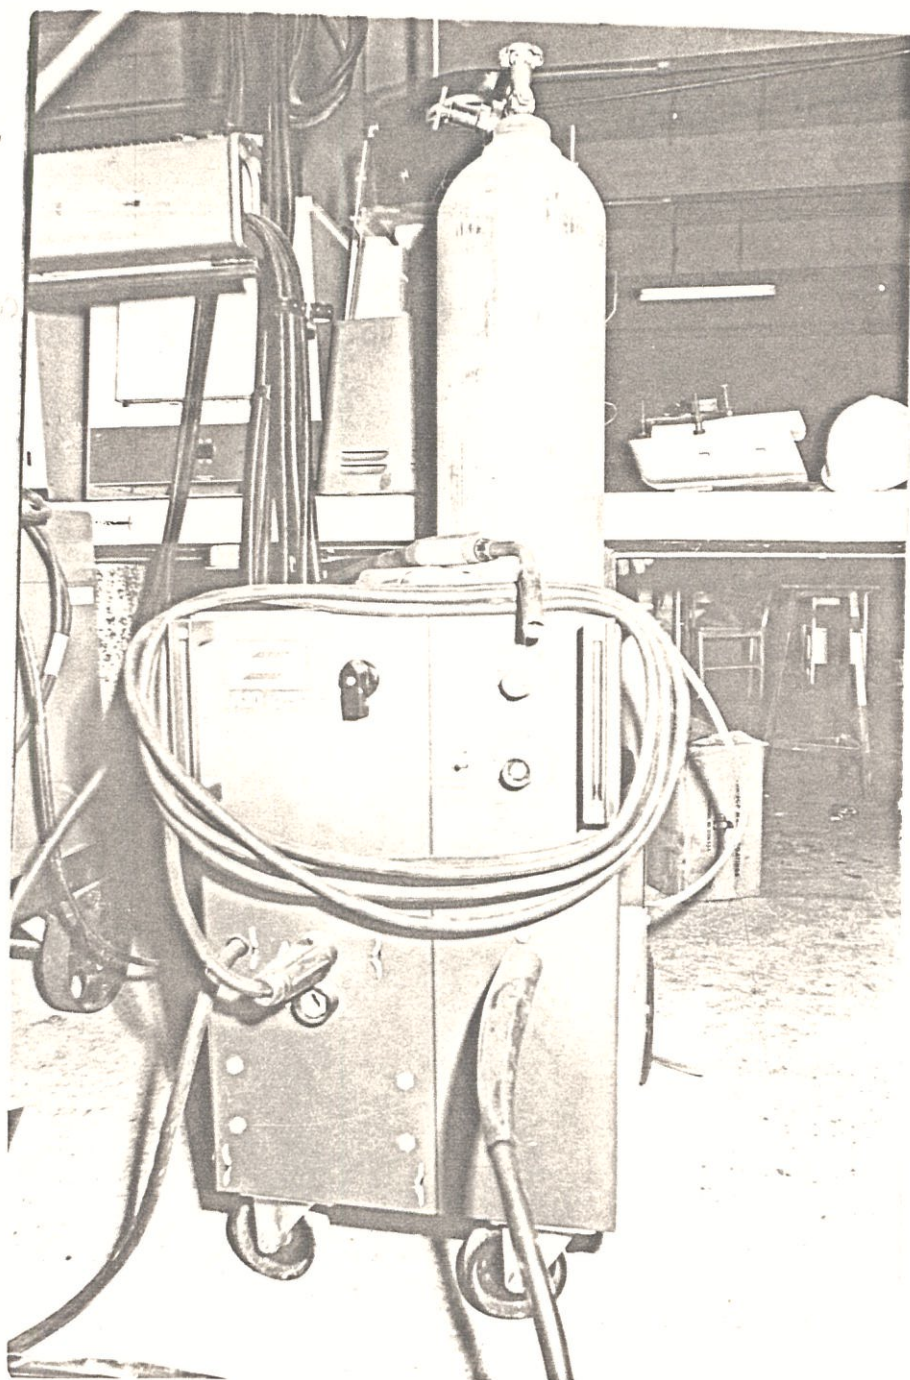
Equipo de soldadura ESAB A-10 - 250 K.
